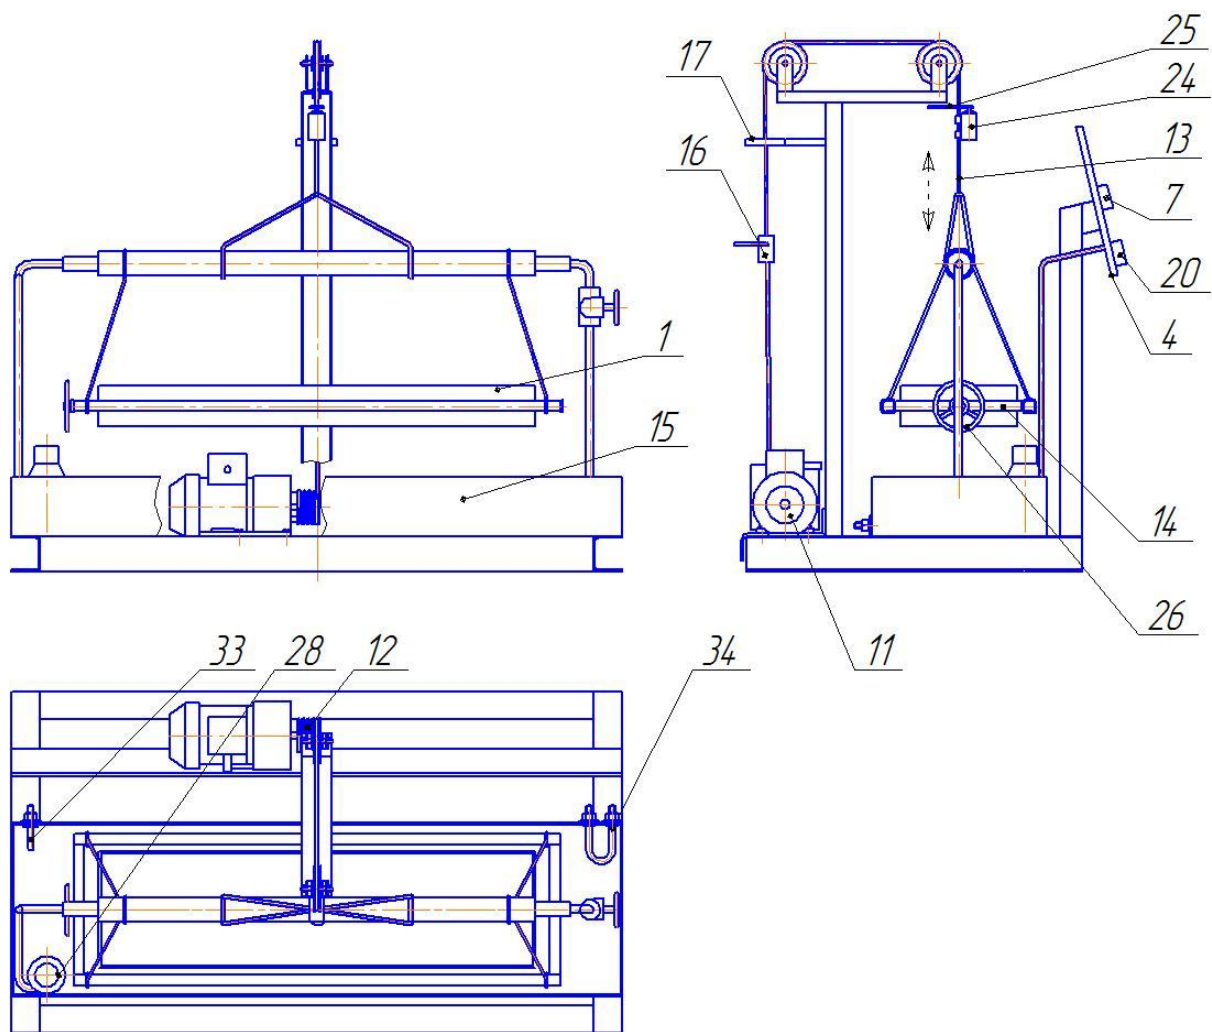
Установка для проращивания зерна: 1 – Емкость; 4 – пульт управления; 7 – реле времени; 11 – мотор-редуктор; 12-катушка; 13 – трос центральный; 14 – рамка; 15 – ванна; 16 – выключатель концевой (рычажного типа); 17 – кольцо; 24 – выключатель концевой (кнопочного типа); 20 – барботер; 25 – пластина подпружиненная; 26 – маховик; 28 – насос; 33 – датчик температуры; 34 – трубчатый электронагреватель ТЭН
